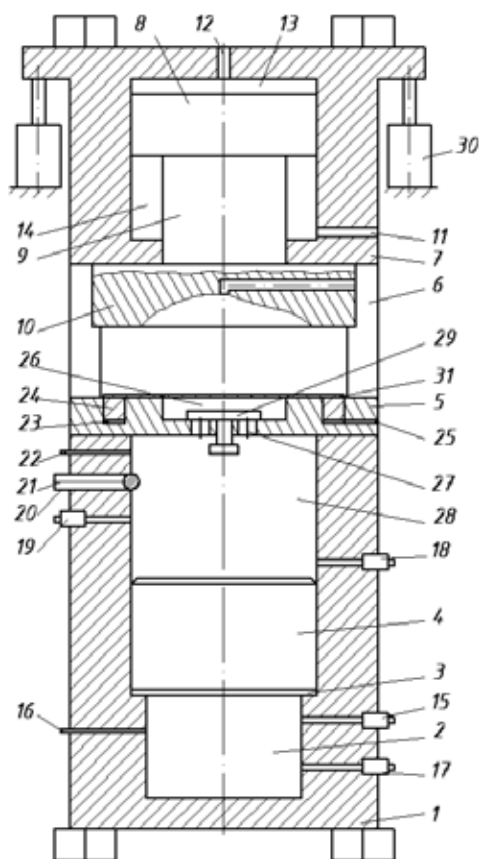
Двухкамерная машина для газовой листовой штамповки
